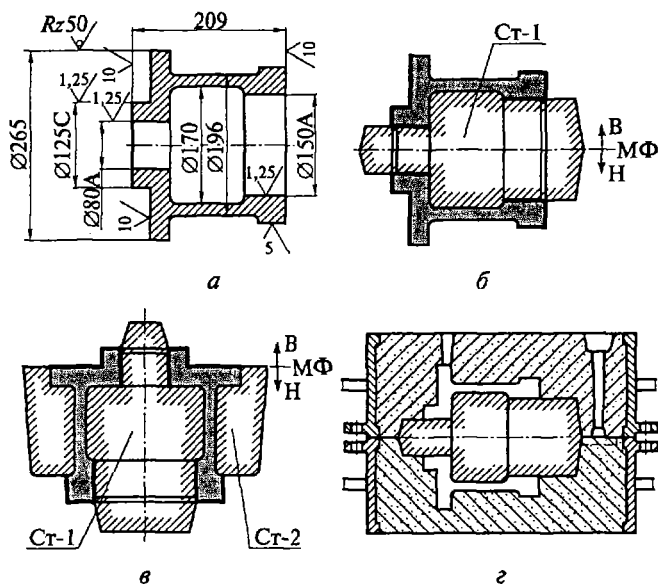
Разработка технологического процесса изготовления отливки корпуса гидромотора:
